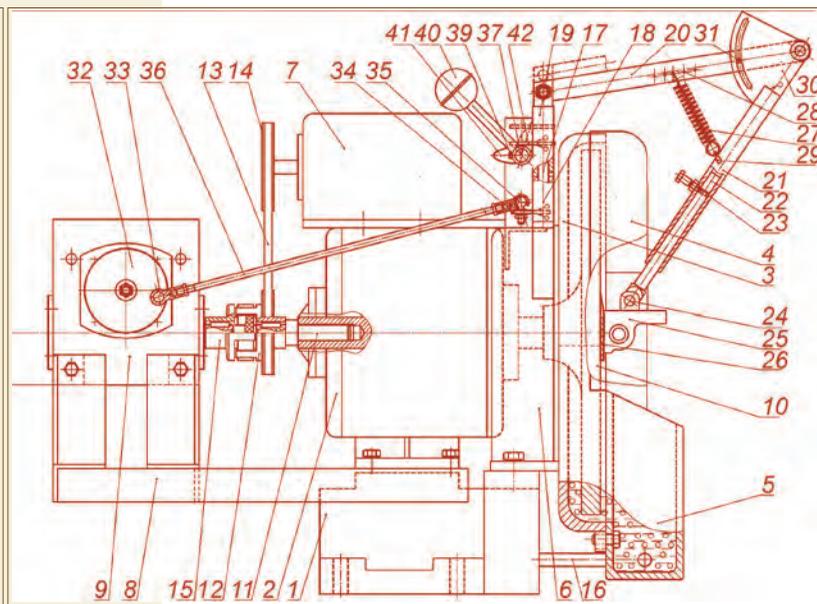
Полуавтомат для заточки режущих пар (вид слева)
